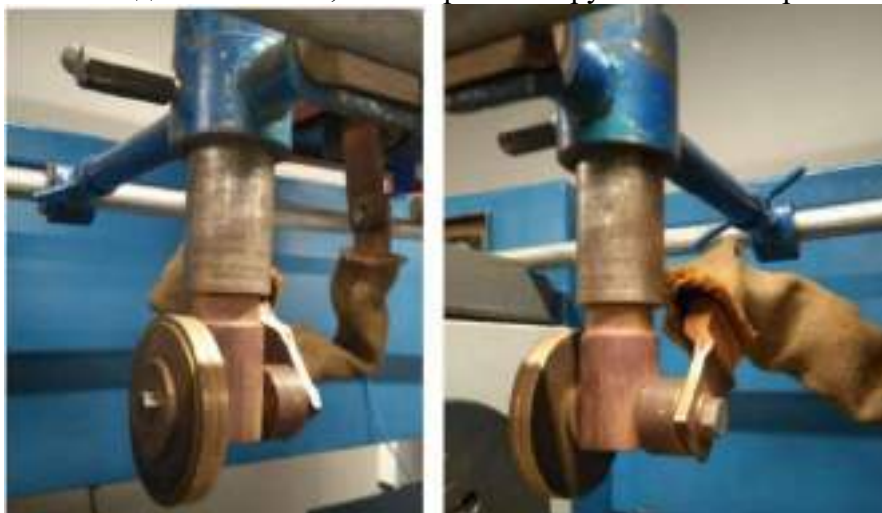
Загальний вигляд і розташування струмопідвідного пристрою на токарно-гвинторізному верстаті
